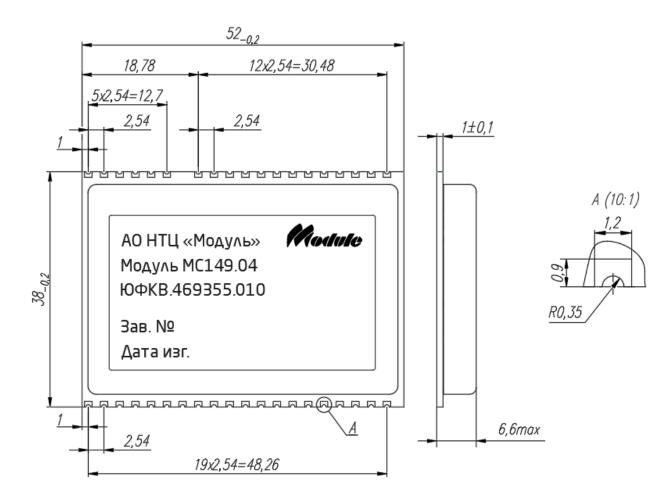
Габаритные и присоединительные размеры Модуля
